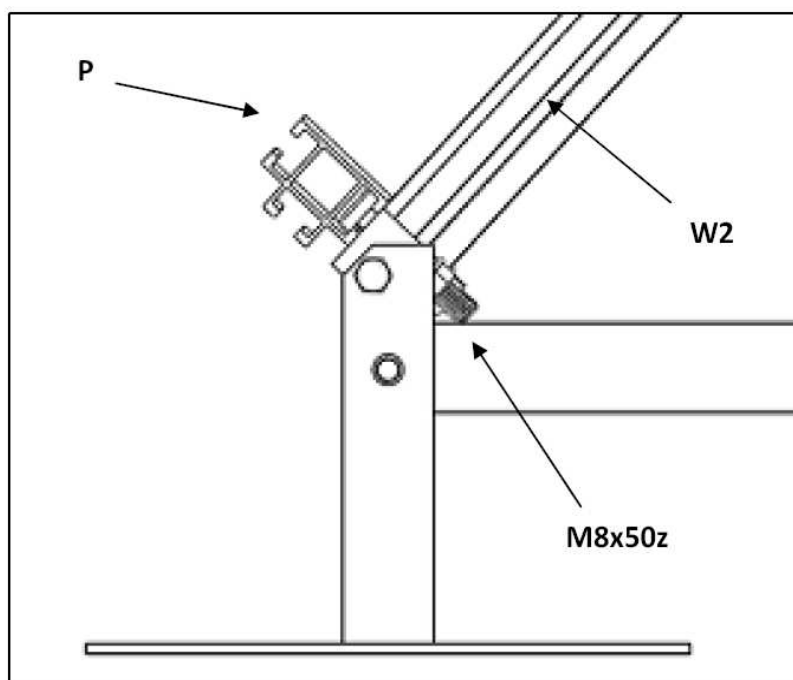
/ Obr. č. 3/ Rys. 3/ Fig. no. 3
